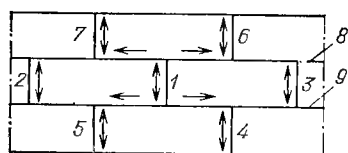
Порядок сварки листовых конструкций.
